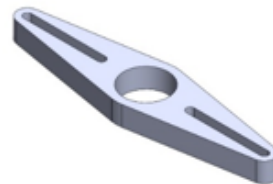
Alat Bantu Pelepas Inner Race Bearing 3D
